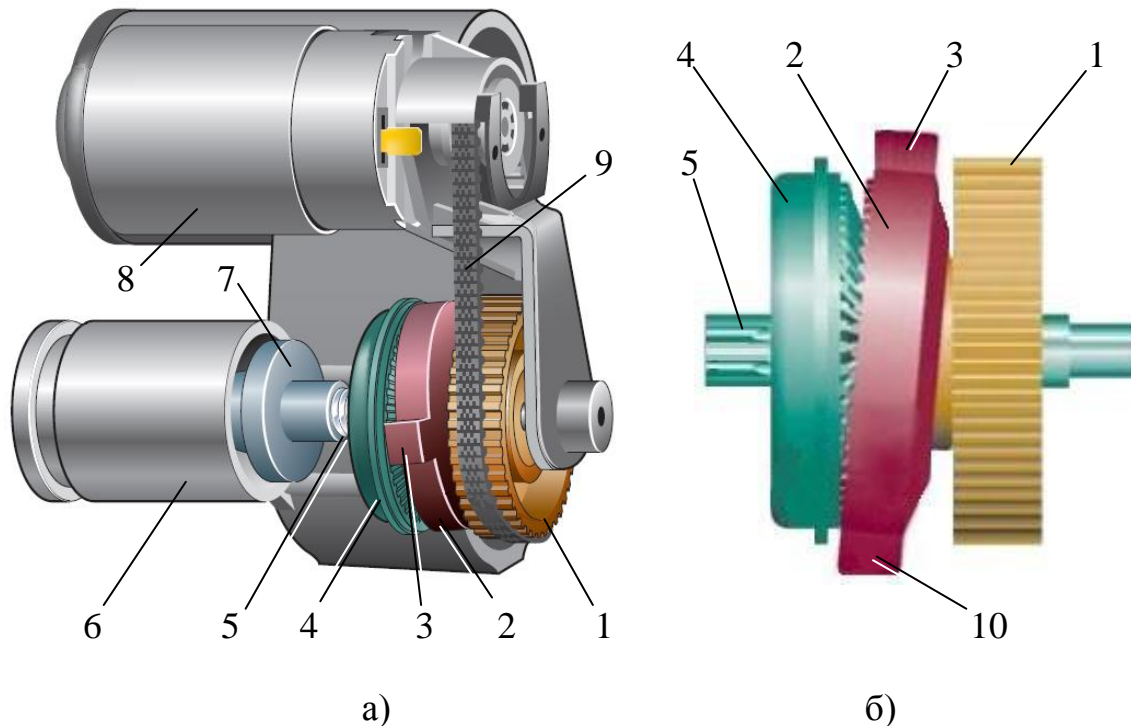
Привод электромеханического стояночного тормоза: а – компоновка привода, б – редуктор с качающейся шестерней; 1 – первичная шестерня редуктора; 2 – качающаяся шестерня редуктора; 3 и 10 – поводки качающейся шестерни; 4 – ведомая шестерня редуктора; 5 – выходной вал редуктора; 6 – поршень рабочей тормозной системы; 7 – винтовая пара; 8 – электродвигатель; 9 – зубчатый ремень
